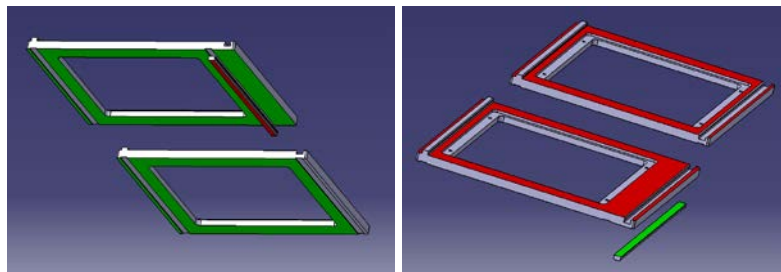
En verde cara de apoyo para la impresión. En rojo cara opuesta a la de impresión.
